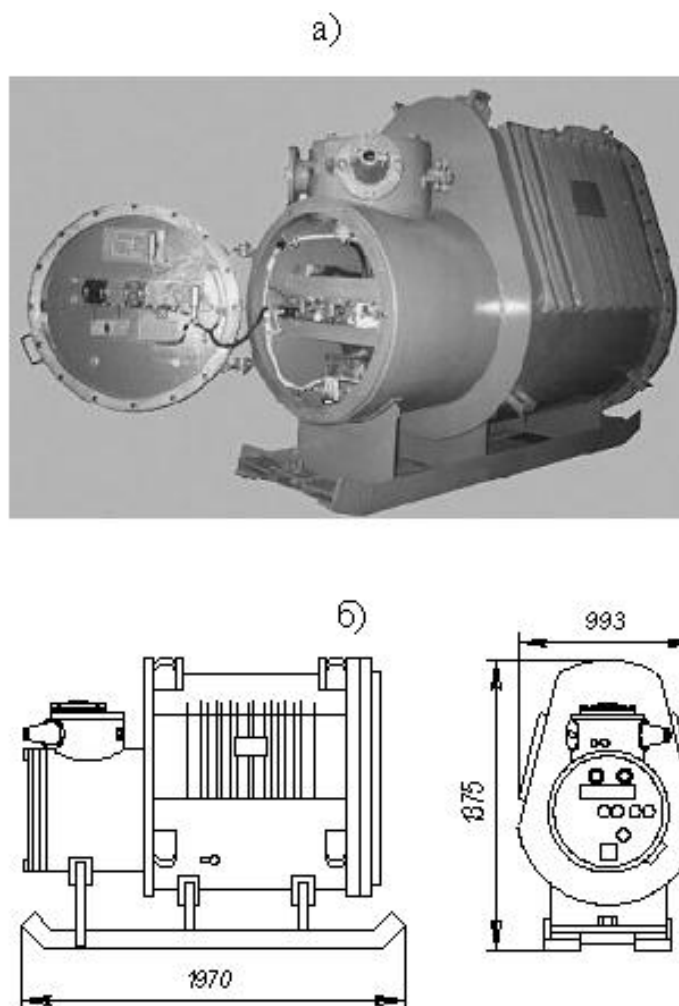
Загальний вигляд (а) і габаритні розміри (б) конденсаторної установки рудничного виконання
